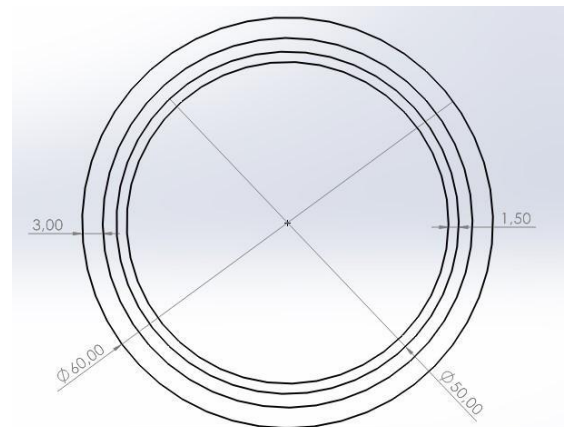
Cotas (em mm), em vista transversal, do corte das camadas que compõem o tubo de pressão.
